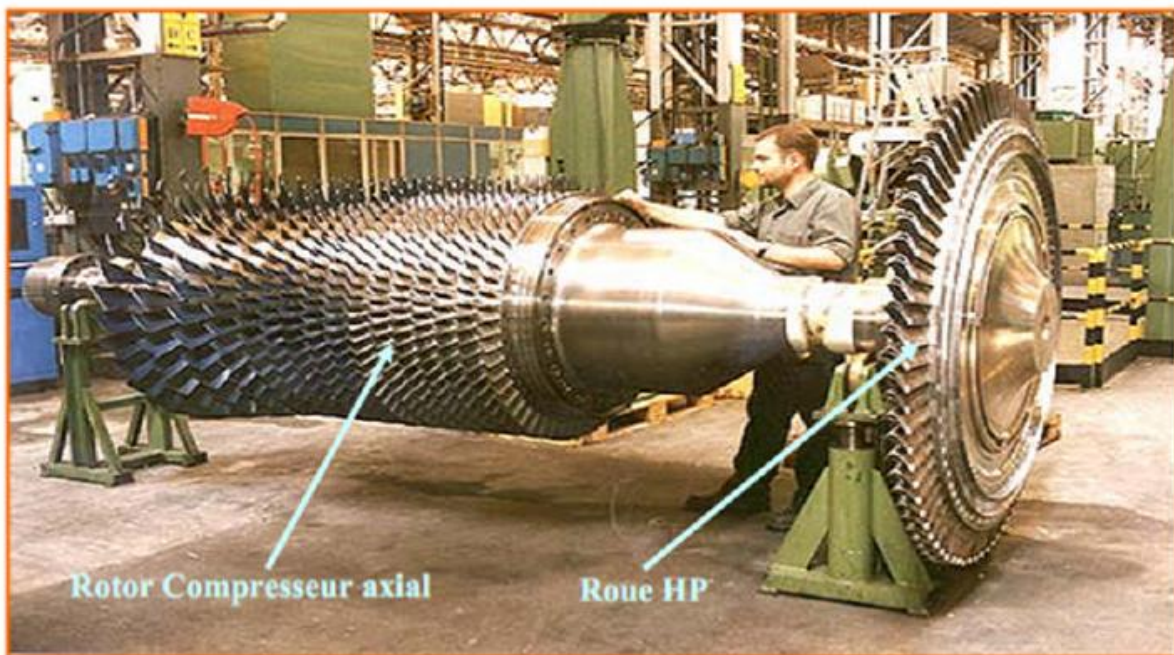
Rotor du compresseur de la turbine à gaz MS 5002C.
